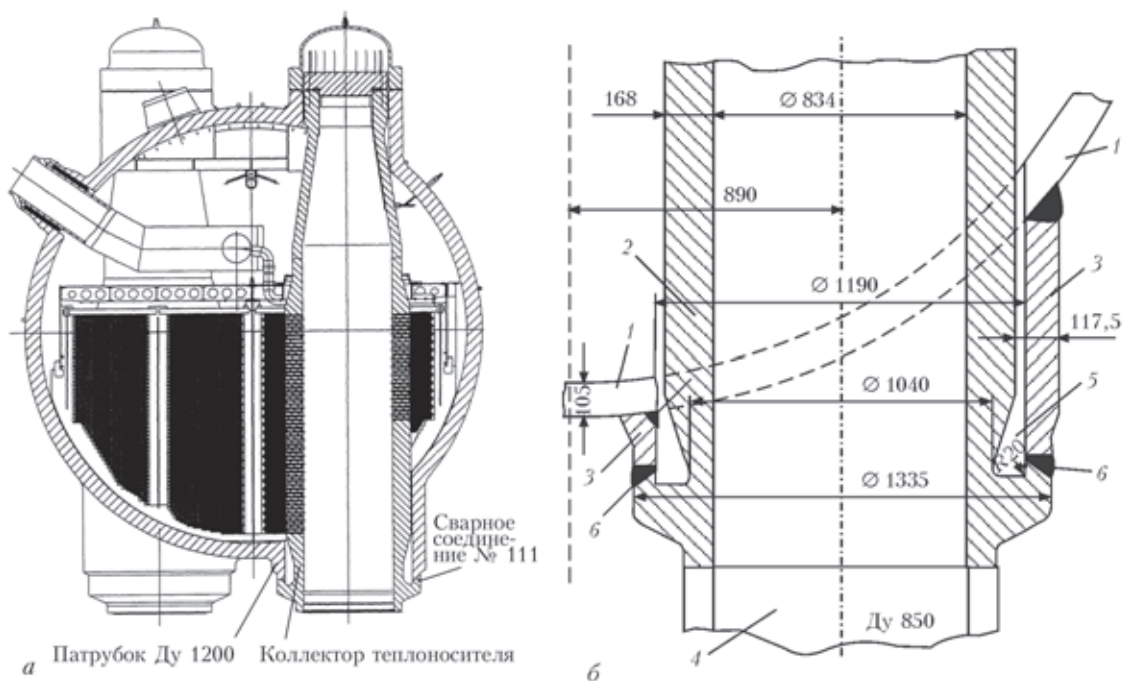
Конструкция парогенератора и узла соединения коллектора с парогенератором: а – фрагмент чертежа ПГВ-1000М; б – схема расположения сварного соединения № 111: 1 – корпус ПГ; 2 – коллектор; 3 – патрубок диаметром 1200; 4 – трубопровод Ду 850; 5 – карман; 6 – сварной шов № 111
